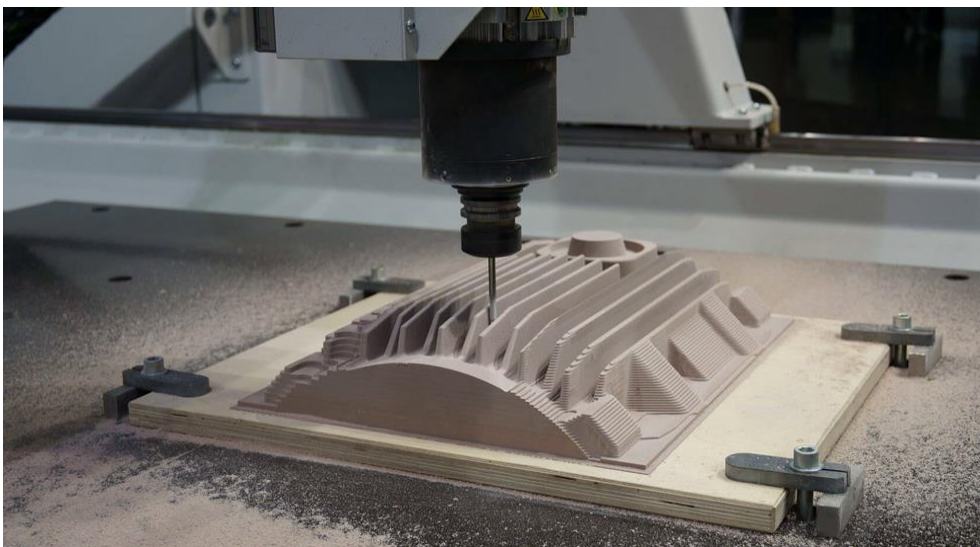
Фрезеровка и ЧПУ-обработка
